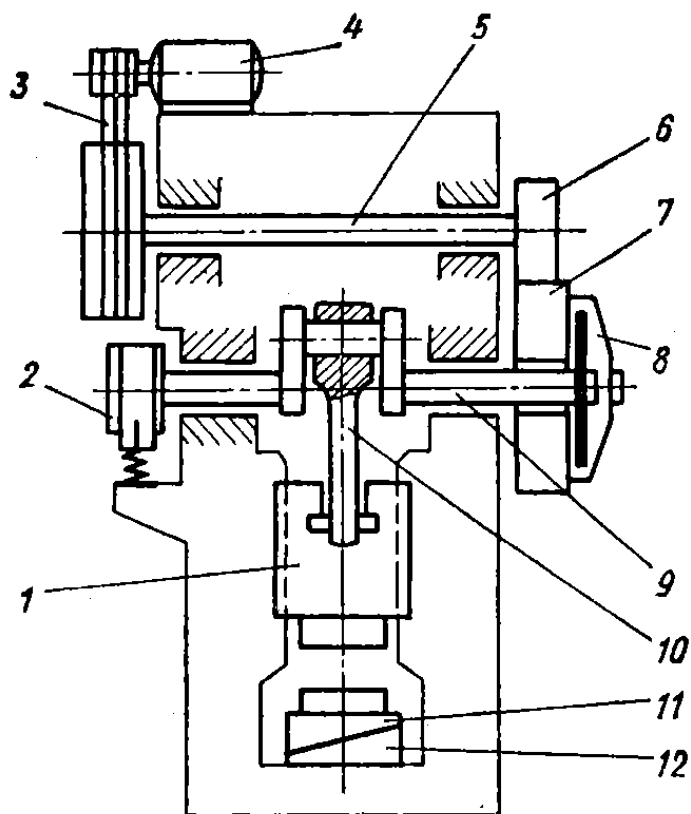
Кинематическая схема кривошипного горячештамповочного пресса
